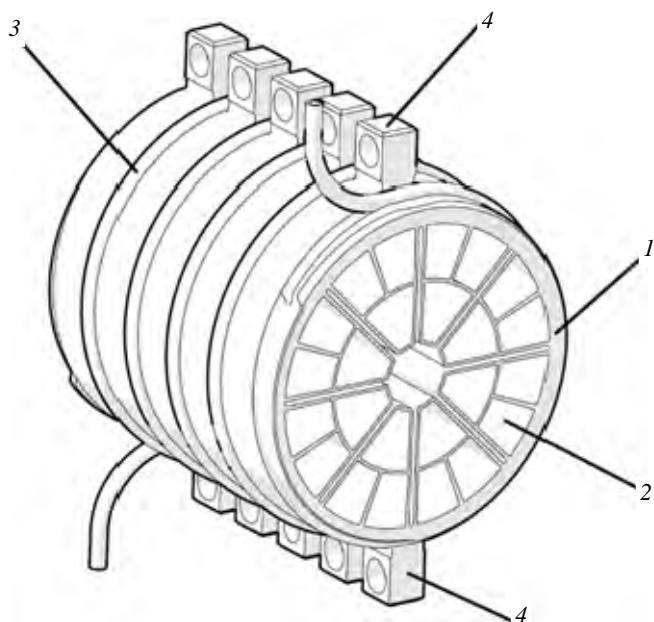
3D-конструкторская модель блока коллиматора с охлаждением: 1 — корпус коллиматора; 2 — трапециевидальные ячейки коллиматора; 3 — трубка водяного охлаждения; 4 — места крепления корпуса к кожуху нейтронной защиты
